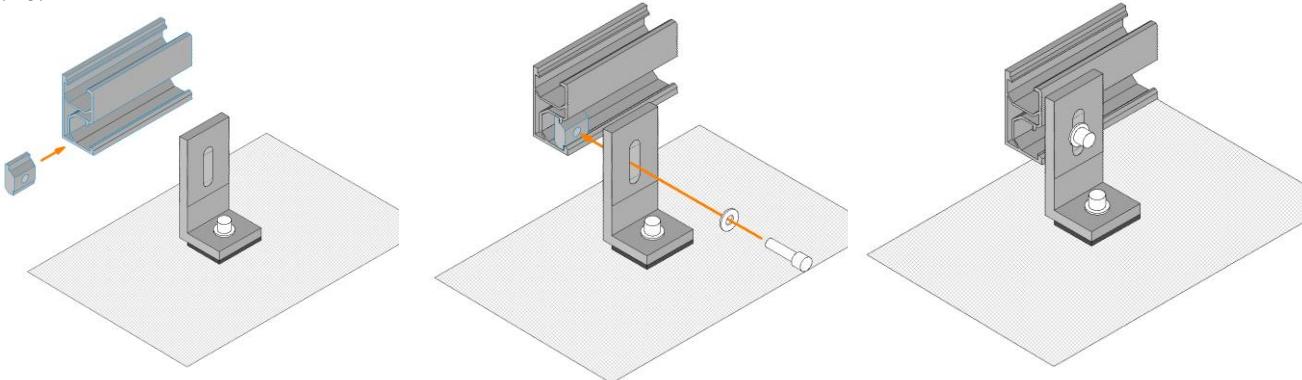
Соединение монтажного профиля и L-образного крепления.
